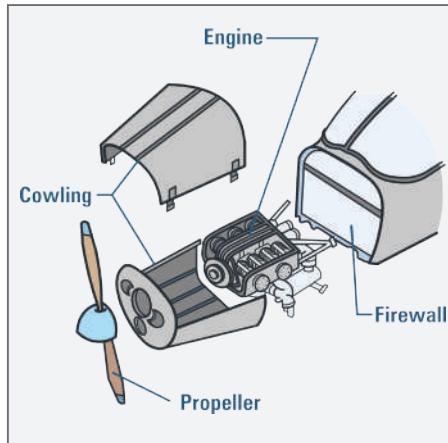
Hélice, motor, parede de fogo e carenagem do motor
